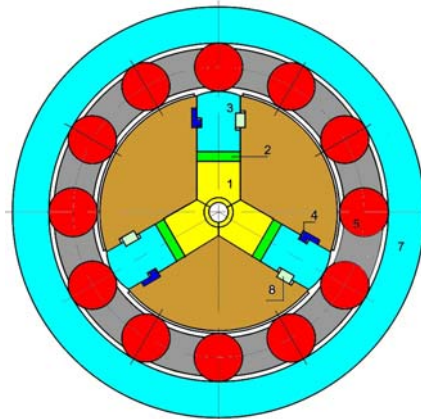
Segmentierung der Werkzeuge in 3 Teile
